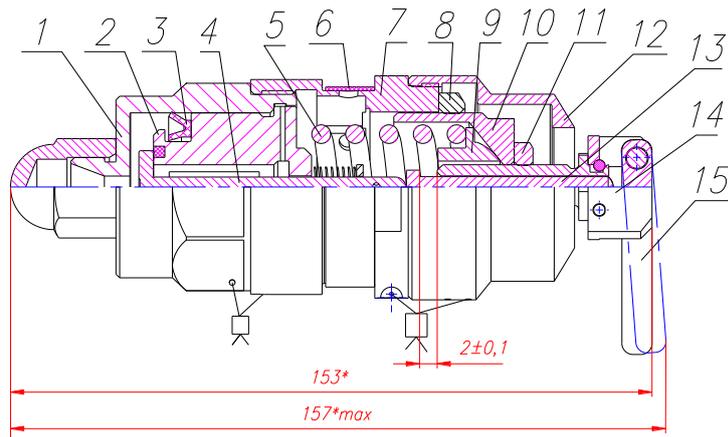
Предохранительный клапан КПП – (3-10): 1 - штуцер, 2 - седло, 3 - манжета, 4 - клапан, 5 - пружина, 6 - кольцо, 7 - корпус, 8 - контргайка крышки, 9 - опора, 10 - крышка, 11 - контргайка упора, 12 - колпак, 13 - толкатель, 14 - упор, 15 - рычаг.
